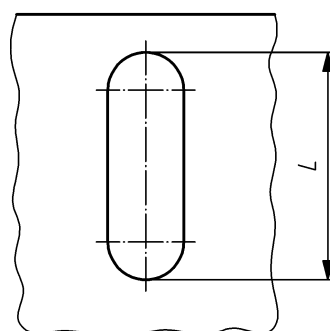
Accès pour le soudage des soudures en bouchons et en entailles
